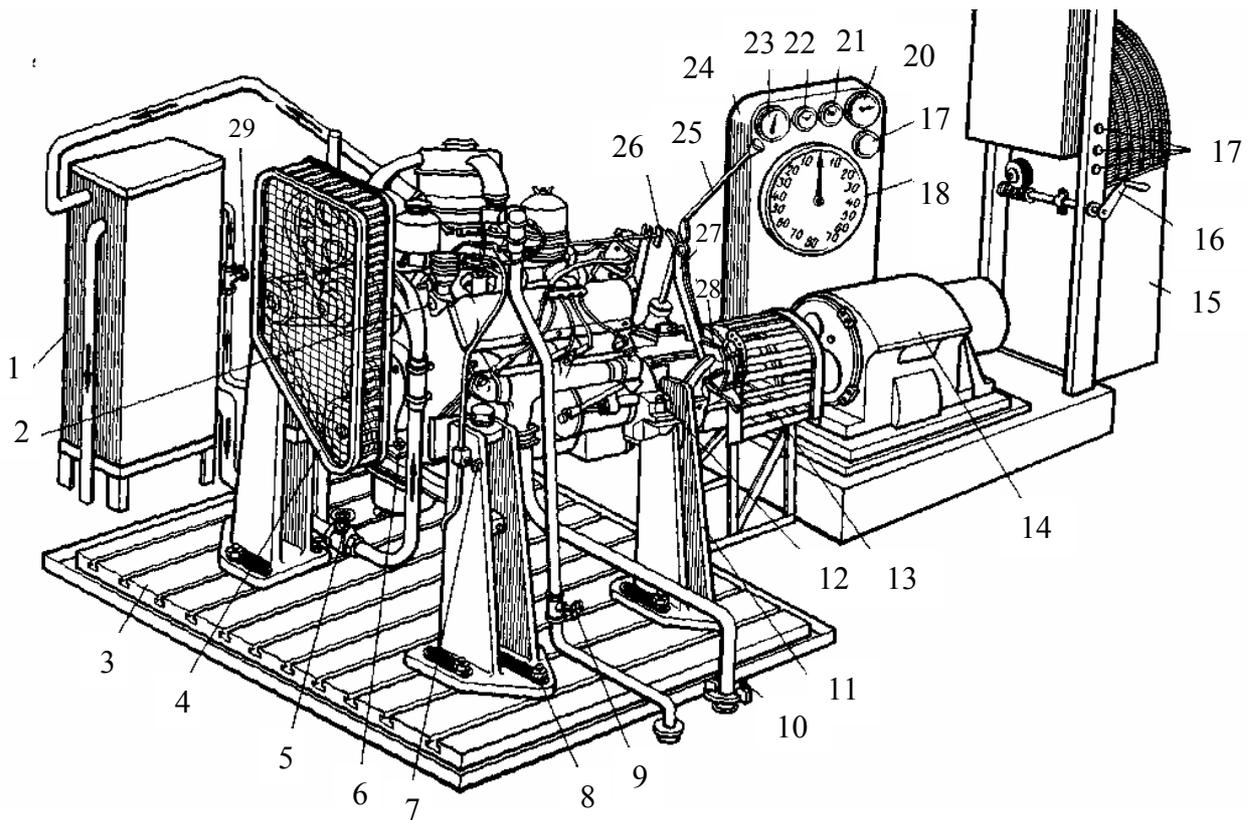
Стенд для обкатки и испытания двигателей: 1 – бак; 2 – двигатель; 3 – плита; 4 и 13 – решетки; 5, 9 и 29 – вентили; 6, 8 и 12 – элементы крепления двигателя; 7 – кран; 10 – элементы крепления газоотводной трубы; 11 – стойка; 14 – электромашин; 15 – реостат; 16 – рукоятка управления реостатом; 17 – кнопки; 18 – шкала; 19 – сигнализатор; 20 – тахометр; 21 и 22 – термометры; 23 – манометр; 24 – корпус; 25 – рычаг коробки передач; 26 – тяга; 27 – рычаг ручного тормоза; 28 – педаль
